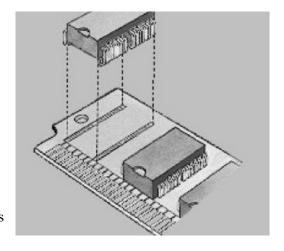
Montaje de los chips en la plaqueta SIMM.
